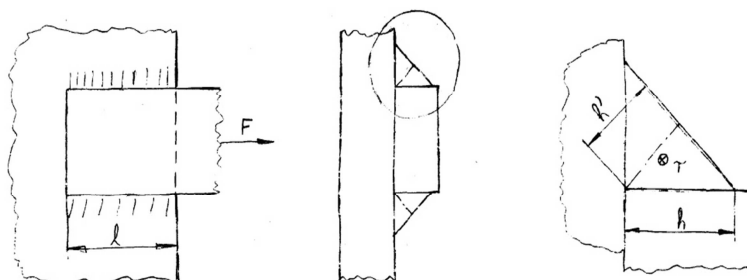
Força paralela ao cordão de soldadura [25]
